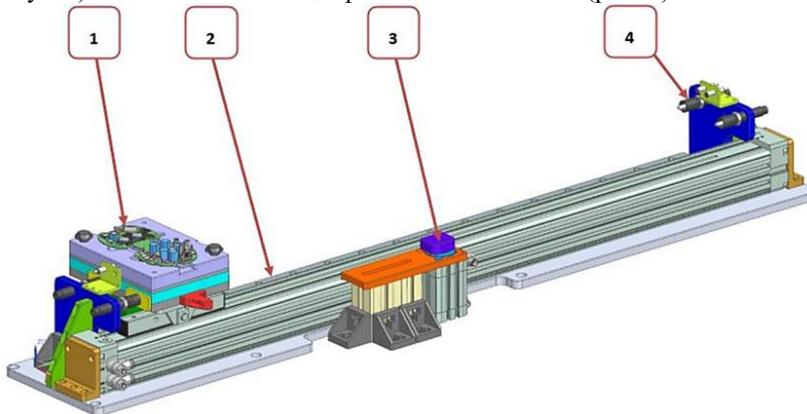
3D CAD-модель запропонованого горизонтального вузла маніпулятора: 1 - станина друкованої плати з її дисплеєм; 2 - лінійний горизонтальний привід по одній осі; 3 - упор станини; 4 - амортизатор
